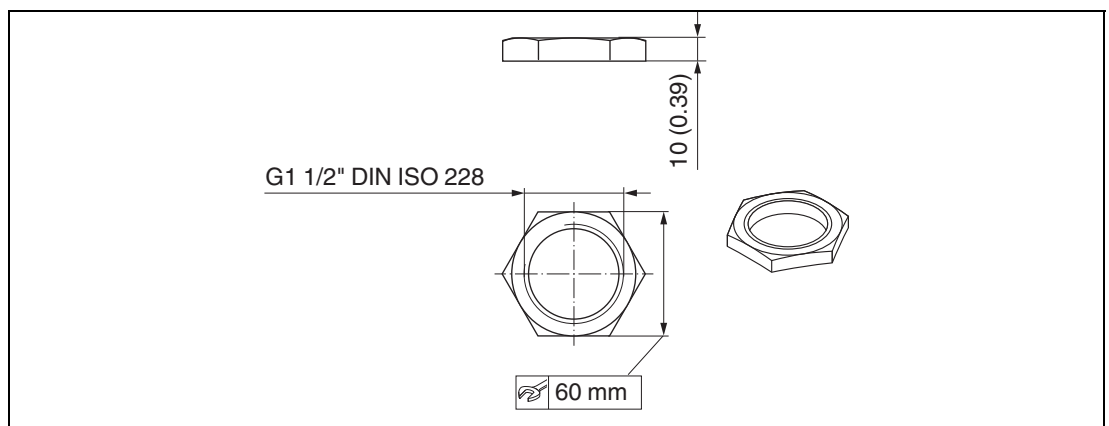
Abmessungen Befestigungsmutter, Maßeinheit: mm (Zoll)
